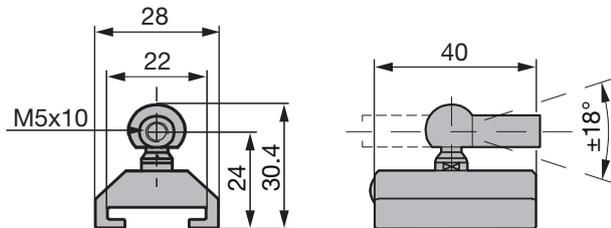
Medidas de montaje del sensor de posición BTL5-F-2814-1S
